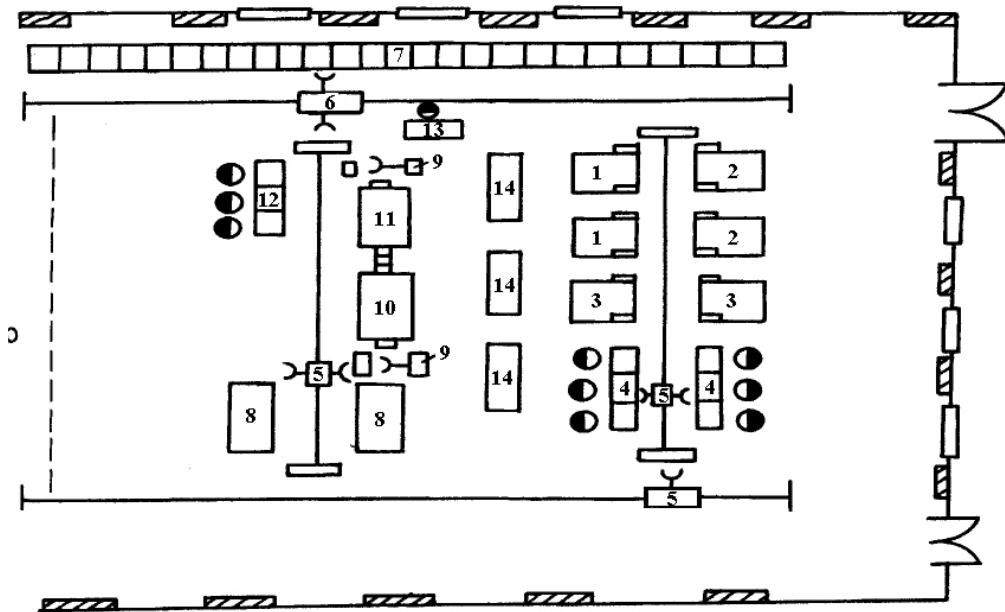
Планировка участка сборки ТЭС с элементами ГАП:
